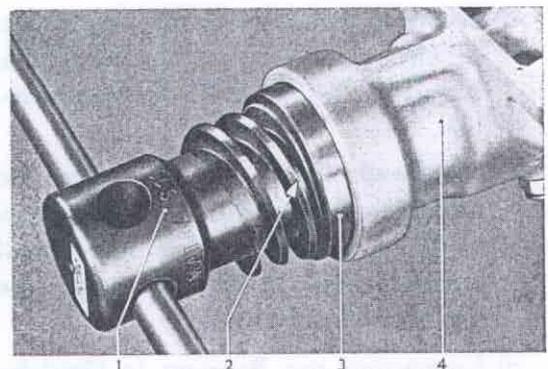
Dichtring mit Auszieher S-1085 aus Getriebegehäuseverlängerung herausziehen
